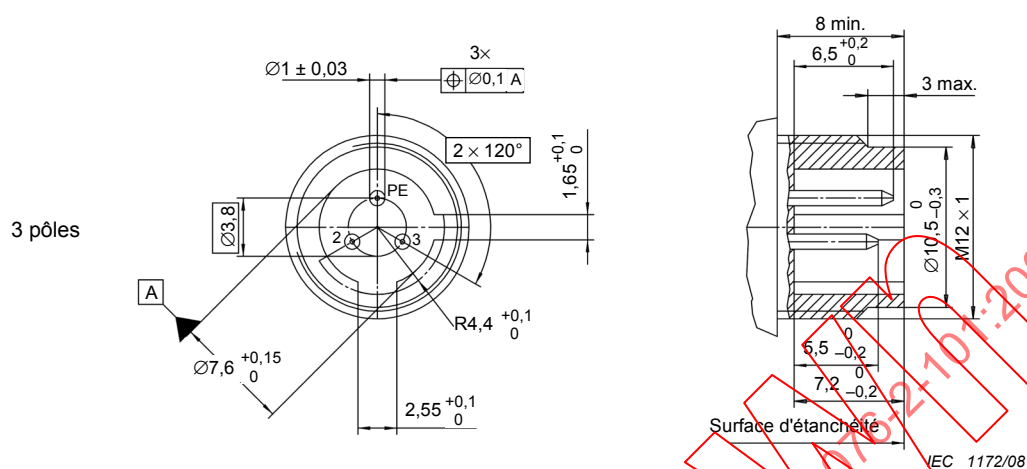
Vue de face du contact mâle, 3 pôles, codage C
